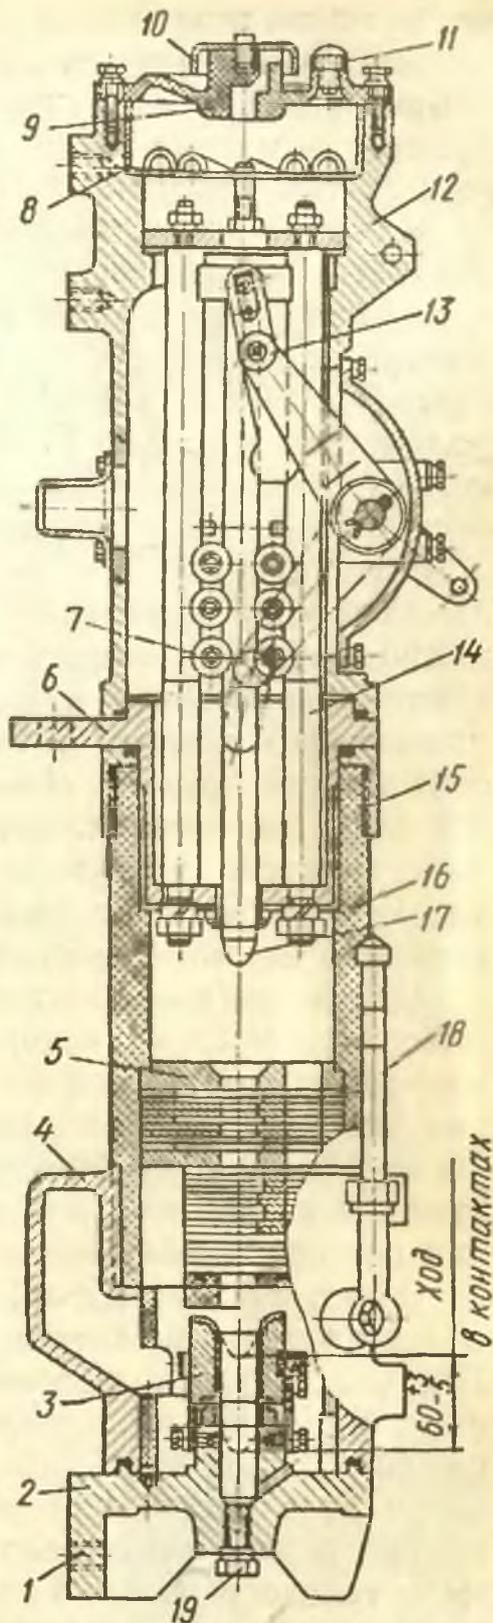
Полюс выключателя на токи 600 и 1000 А:
